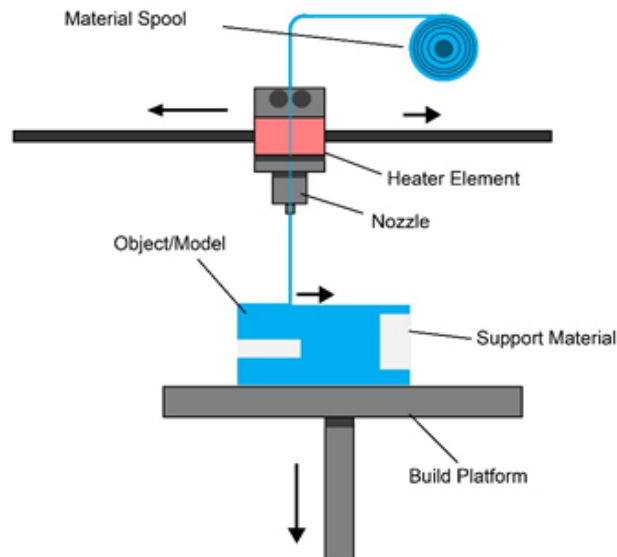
Método de impresión 3D basado en extrusión. Extraído de [49].
